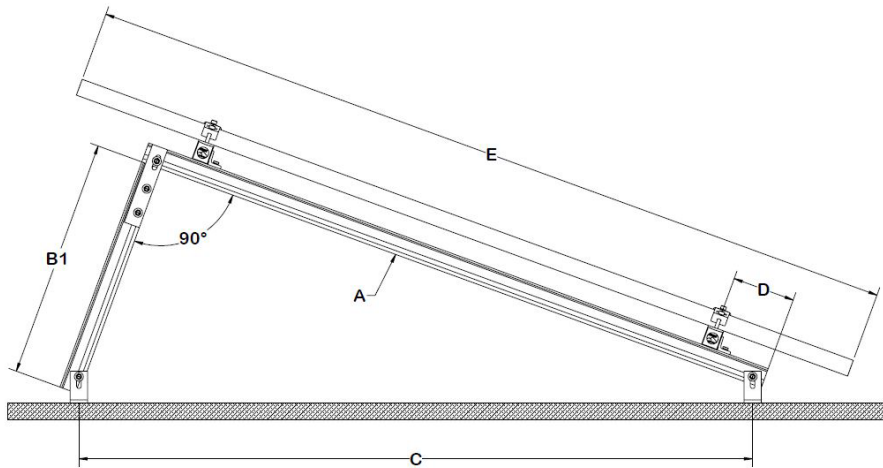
Dimensiones de ensamble para sistema de 1 fila.
